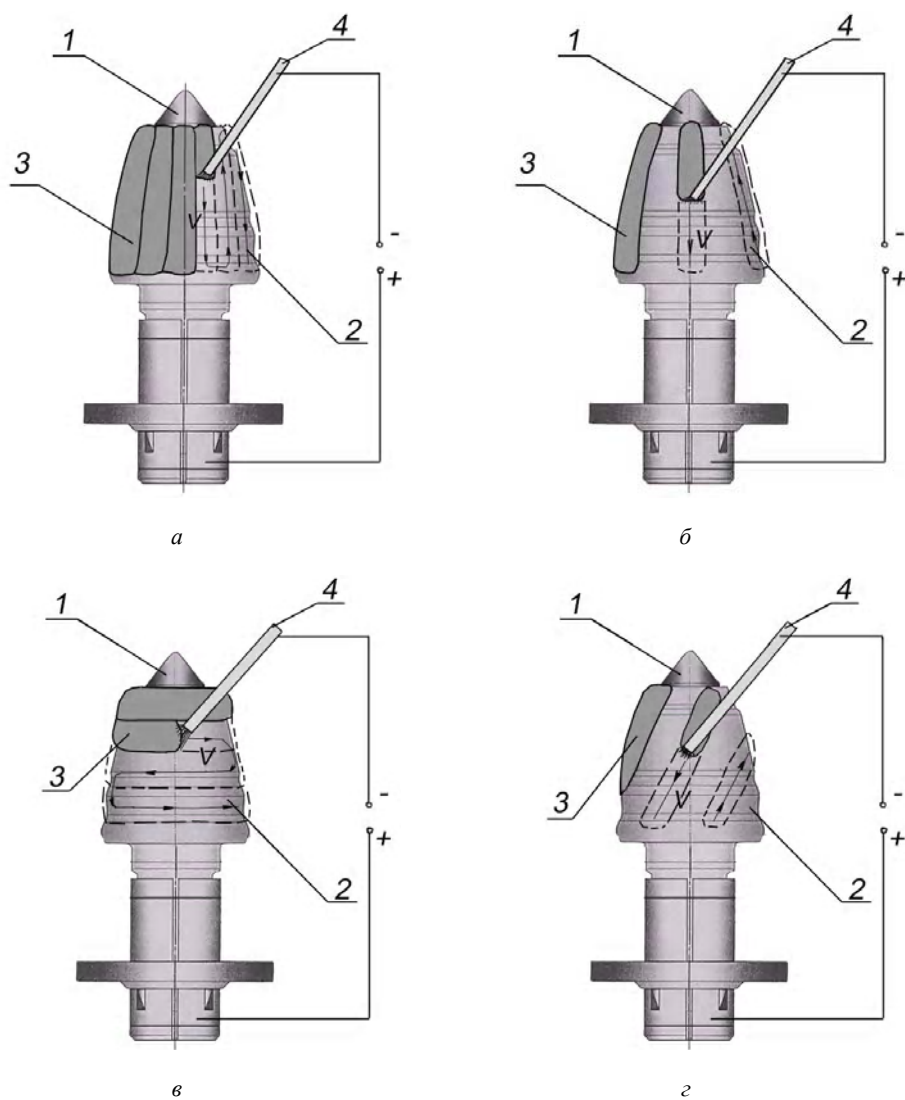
Технологические схемы наплавки резцов дорожных фрез: *а* – параллельно оси резца, *б* – параллельно оси резца с зазорами, *в* – под углом к оси резца, *г* – спиралевидная наплавка: 1 – наконечник резца; 2 – корпус резца; 3 – наплавленный металл; 4 – контуры наложения валиков; *V* – направление наплавки
